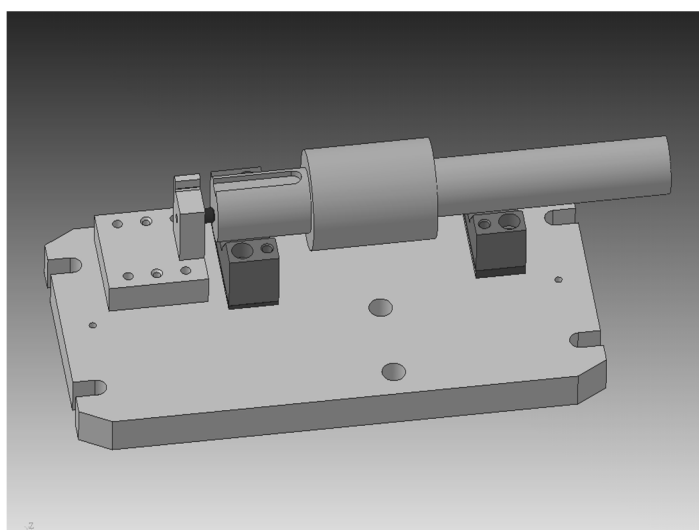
Установлення деталей для запобігання повздовжнього зсуву вала
